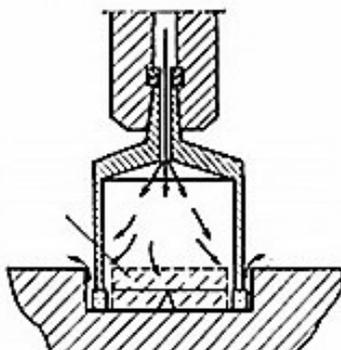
Схема сверления камня кольцевым сверлом с подачей СОЖ
